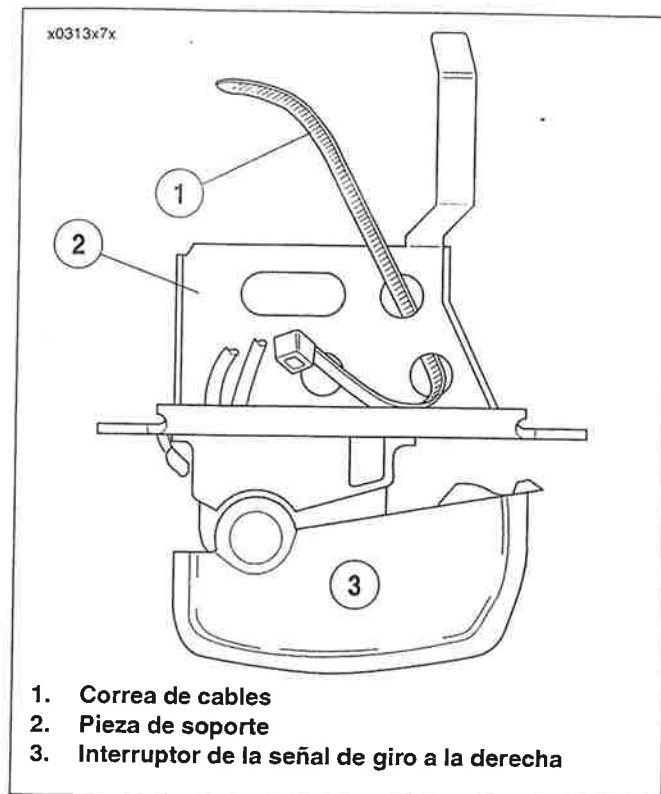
Insertar la correa de cables en la pieza de soporte del interruptor
